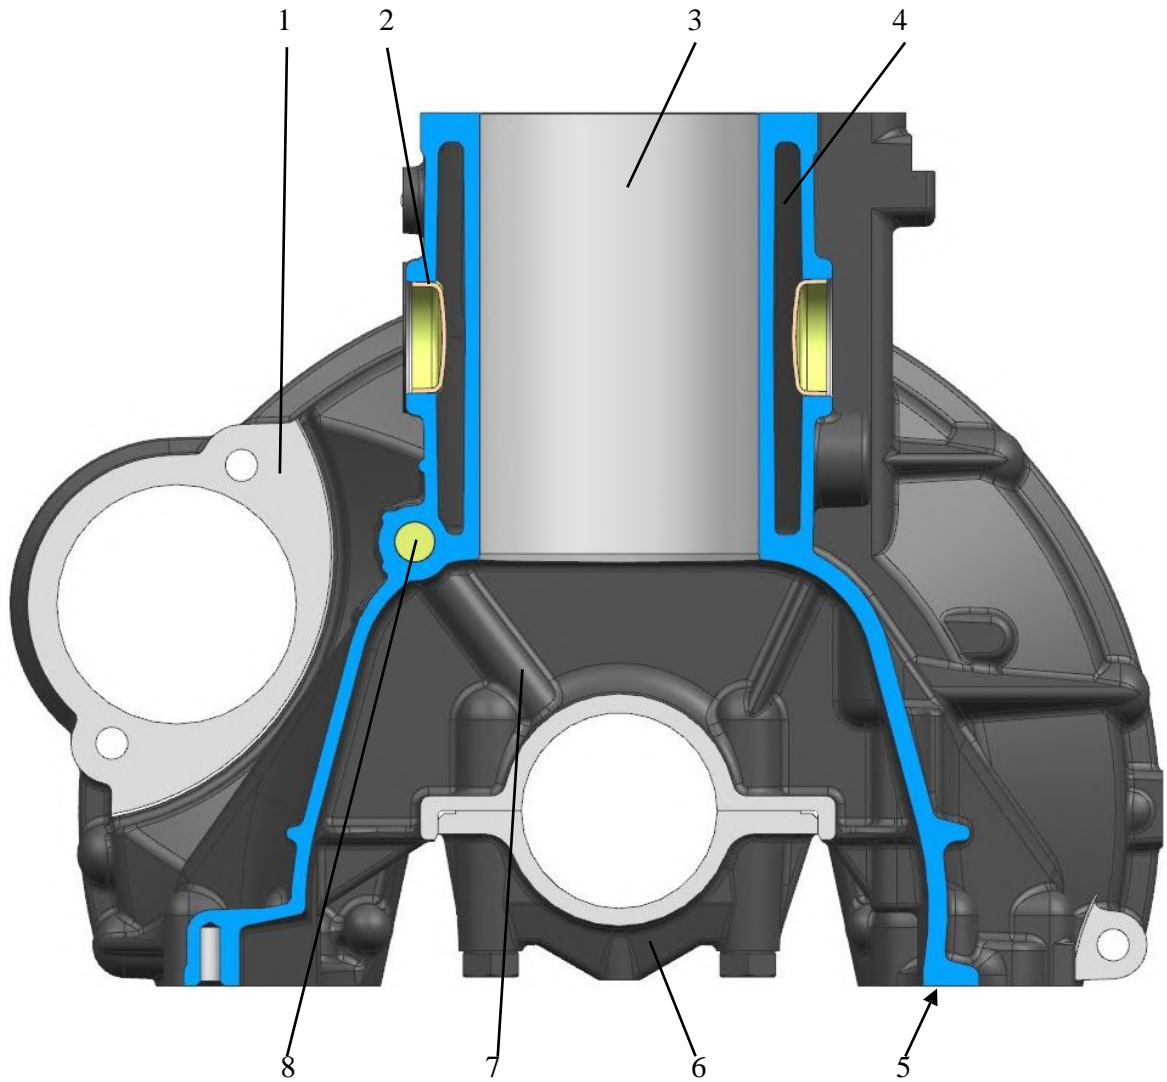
Zylinderblock. Querschnitt entlang der Zylinderachse:
